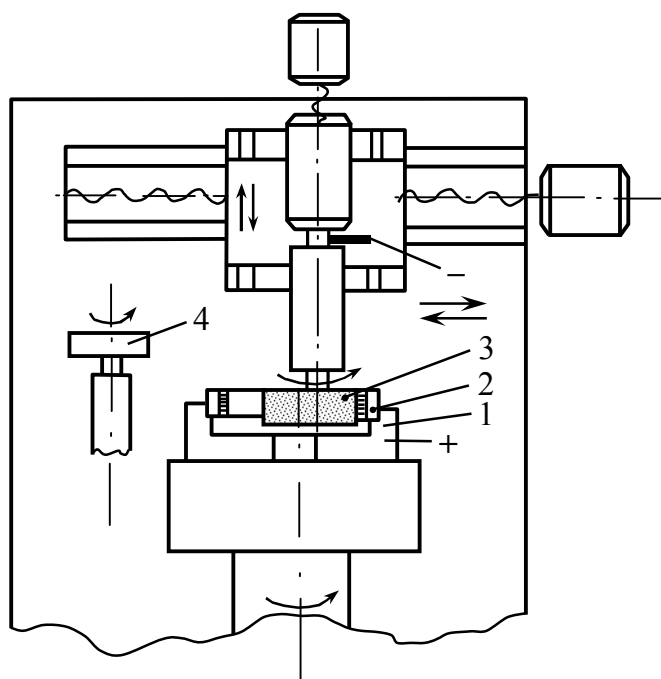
Схема модернизированного токарно-карусельного станка для электроабразивного шлифования сотовых уплотнений:
